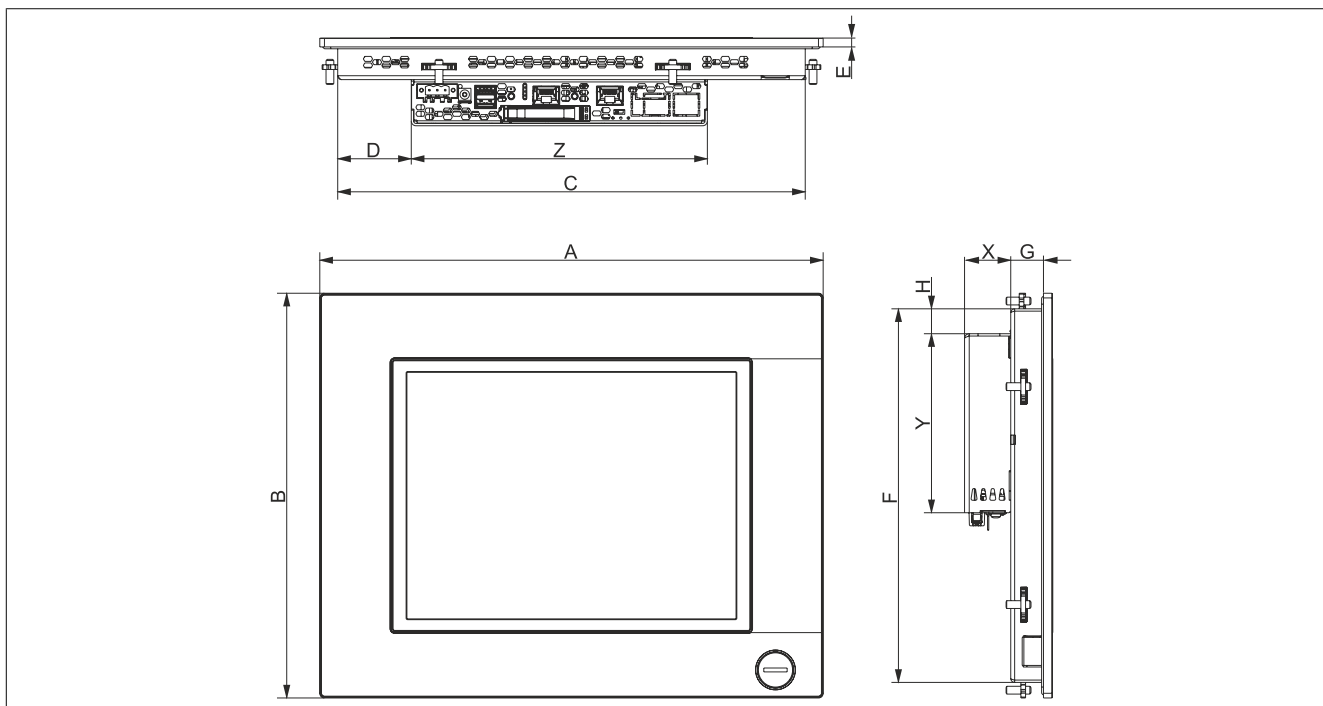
Abmessungen - Panel PC 2100 mit AP1000 Panels mit Halteklammern (Beispielabbildung)
